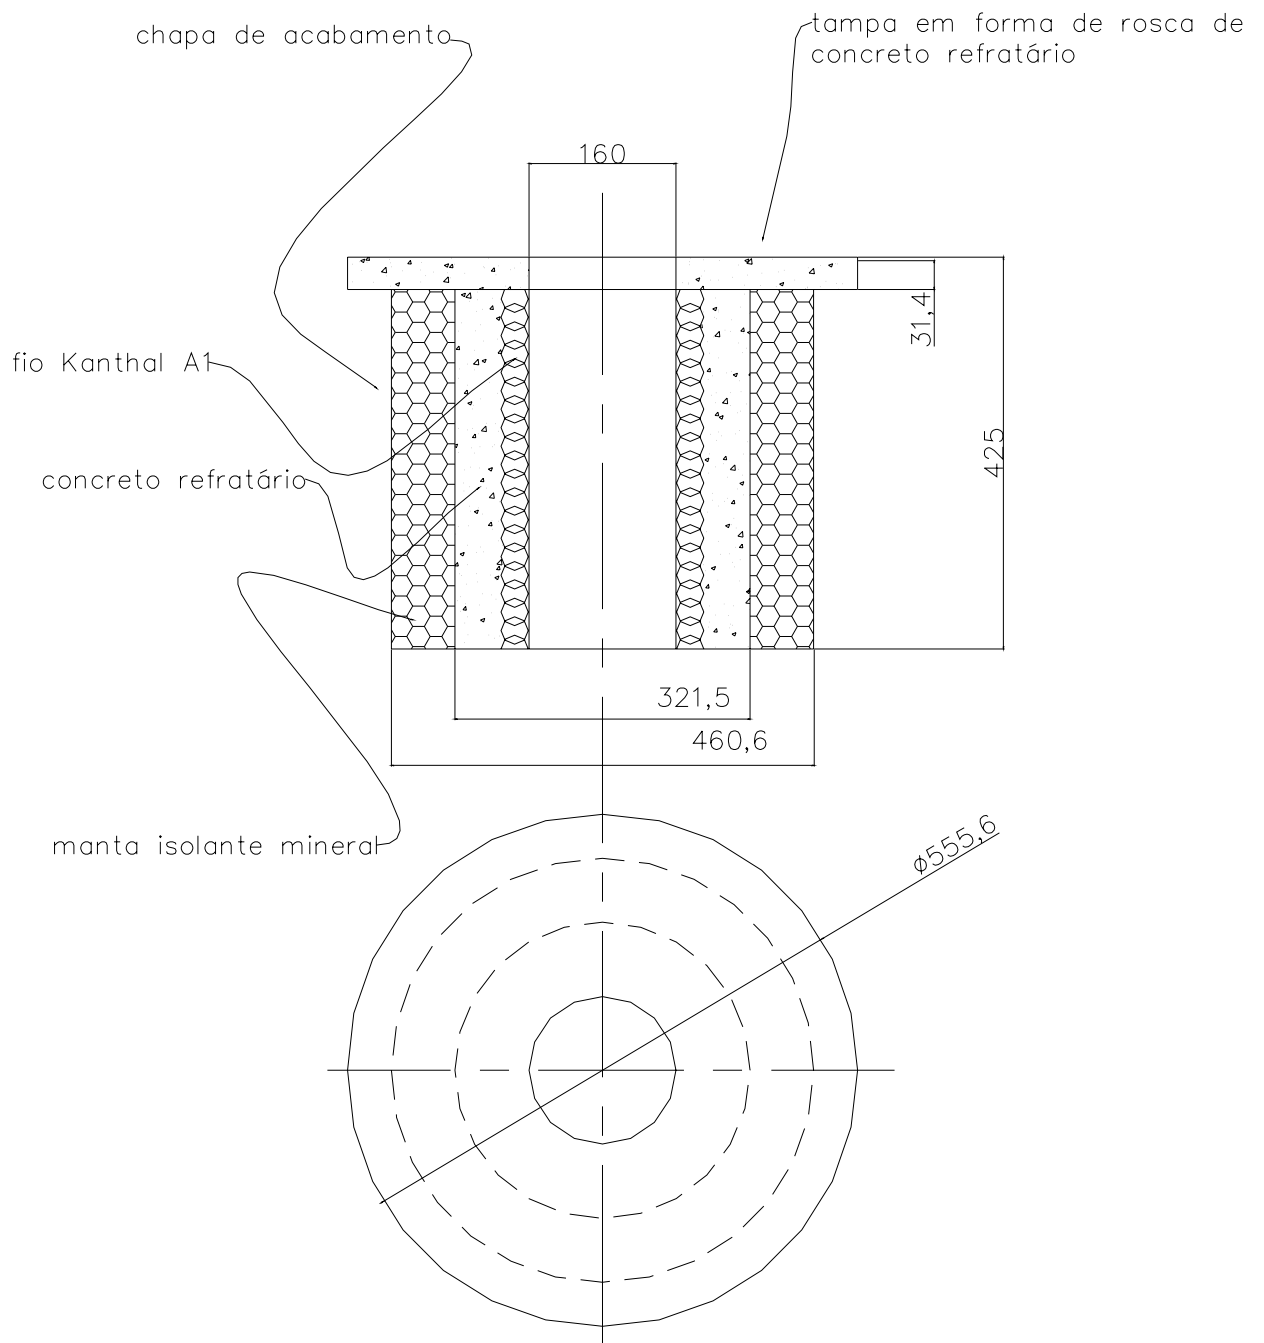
Desenho do forno (dimensões em milímetros)
